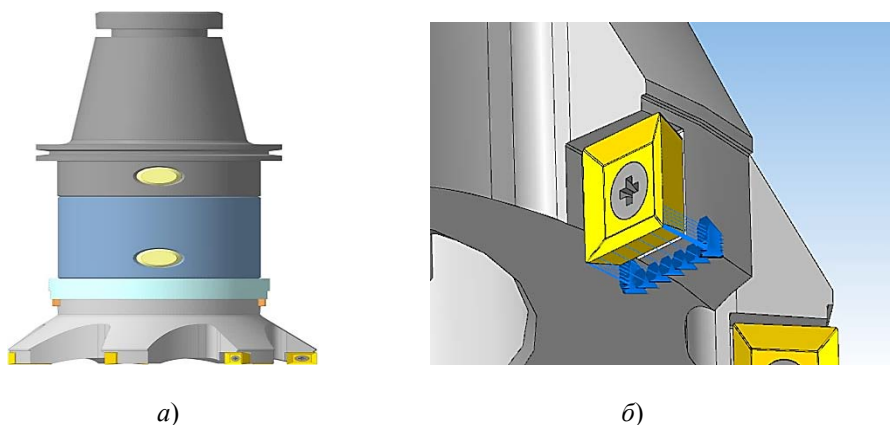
3D-модель торцевой фрезы F90SD D125-40-CP12 (а) и схема воздействия силы P_z на режущую пластину (б)
